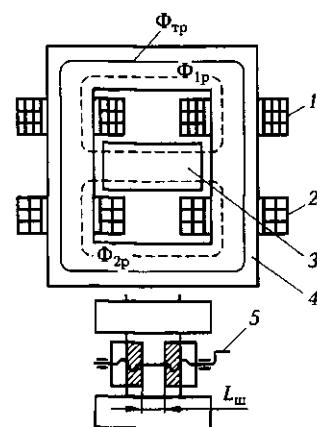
Конструктивная схема сварочного трансформатора серии СТШ:
